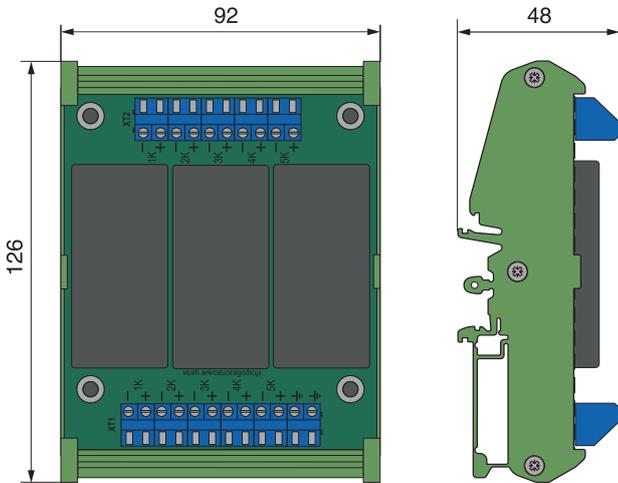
Габаритные размеры барьеров ЭНИ-БИС-112, 114-Ex-DIN
